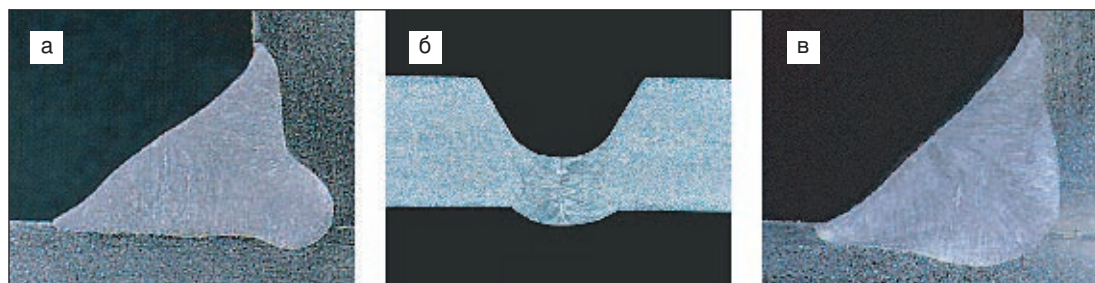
Макрошлифы швов, сваренных сплошной (а) и порошковой (б, в) проволокой диаметром 1,2 мм: а — узкая дуга образует глубокое «пальцеобразное» проплавление, которое имеет высокую вероятность образования дефектов сплавления; б — хорошее проплавление корня и равномерное смачивание свариваемых кромок сопоставимо со сваркой на керамической подкладке; в — широкая дуга обеспечивает однородную (благоприятную) форму проплавления обеих деталей и плавный профиль шва
